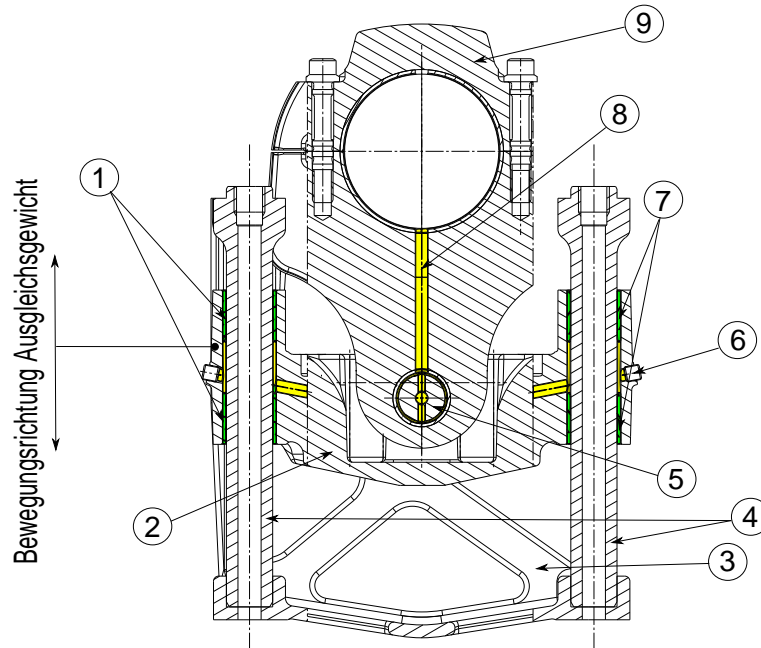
Schnitt der Gesamtansicht des Massenausgleiches, [16]
